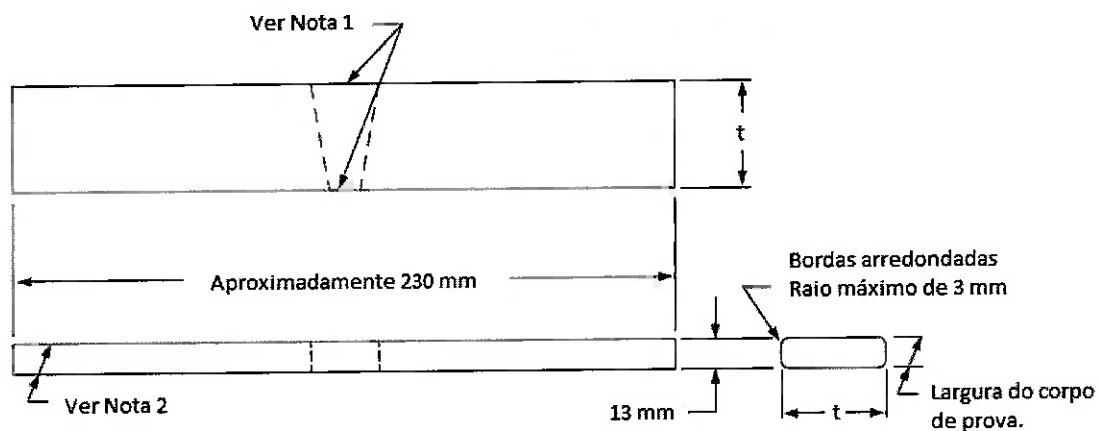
Corpo de Prova para ensaios de Dobramento de Face ou de Raiz conforme API 1104 [3].
